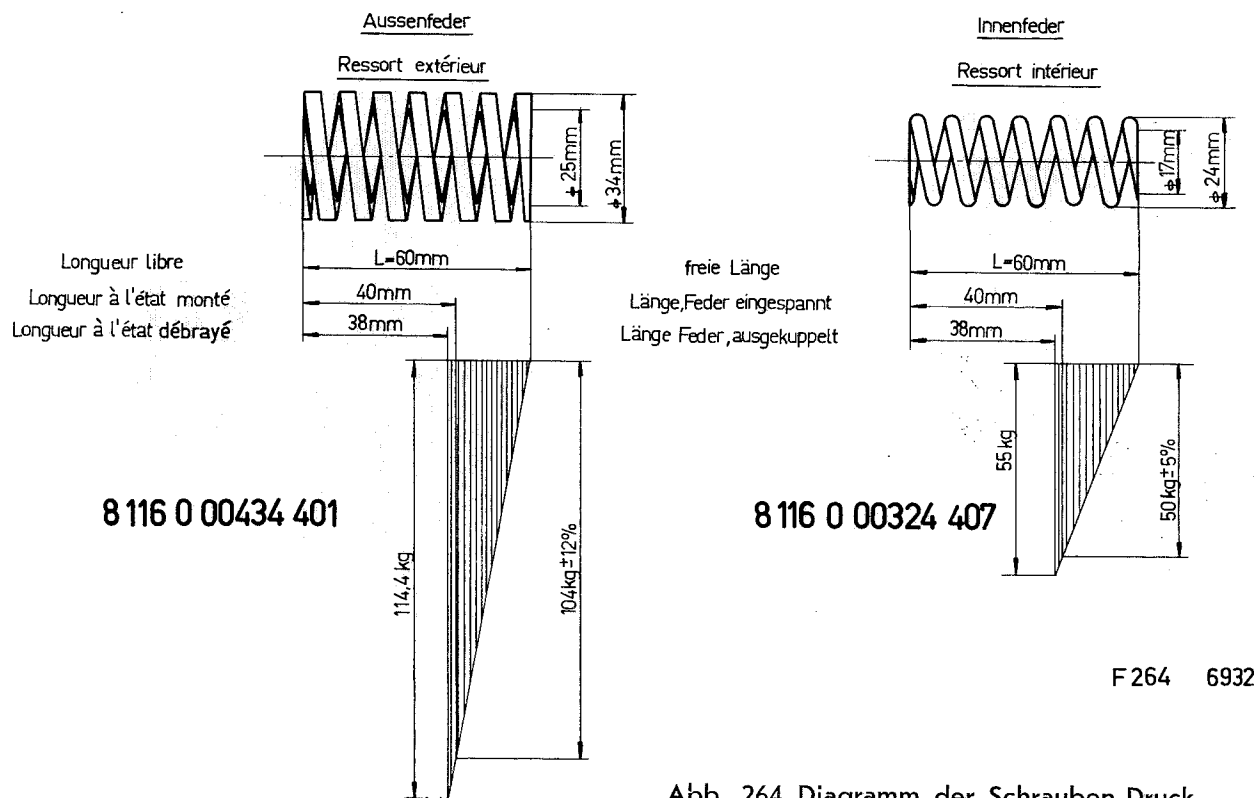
Diagramm der Schrauben-Druckfedern für die Kupplung
